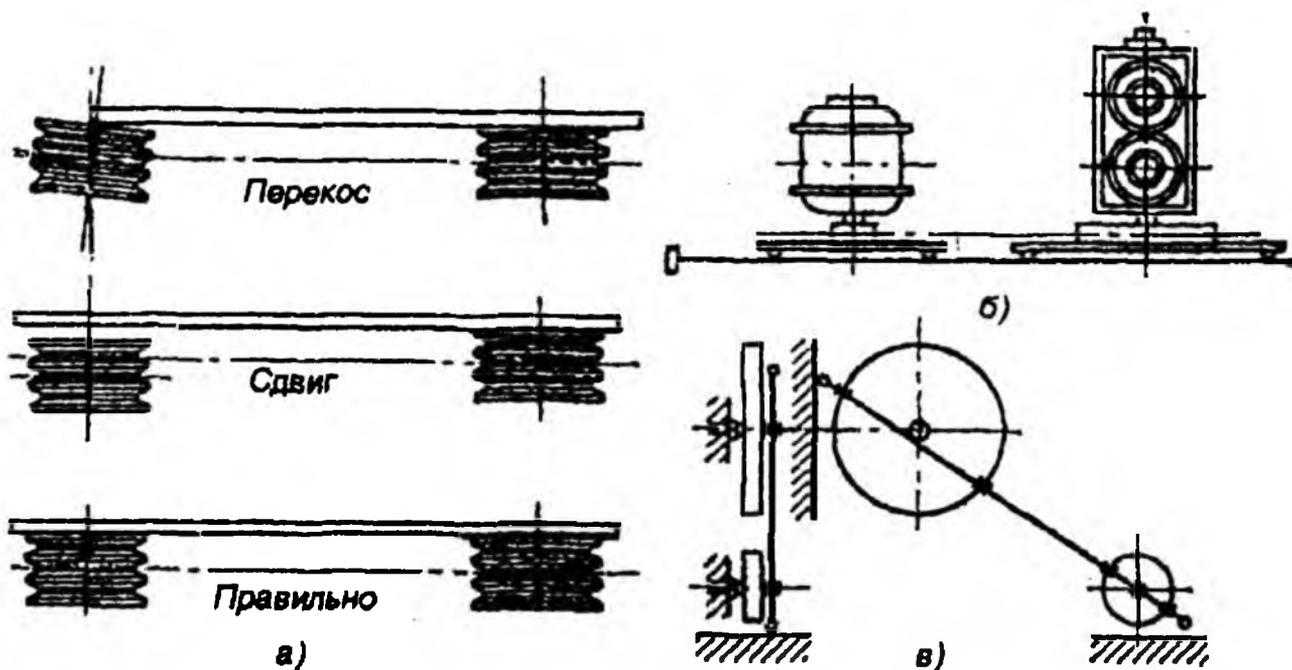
Способы выверки установки электродвигателя при ременной и клиноременной передачах и одинаковой ширине шкивов с помощью линейки (а), скоб и струны (б), шнура(в)
